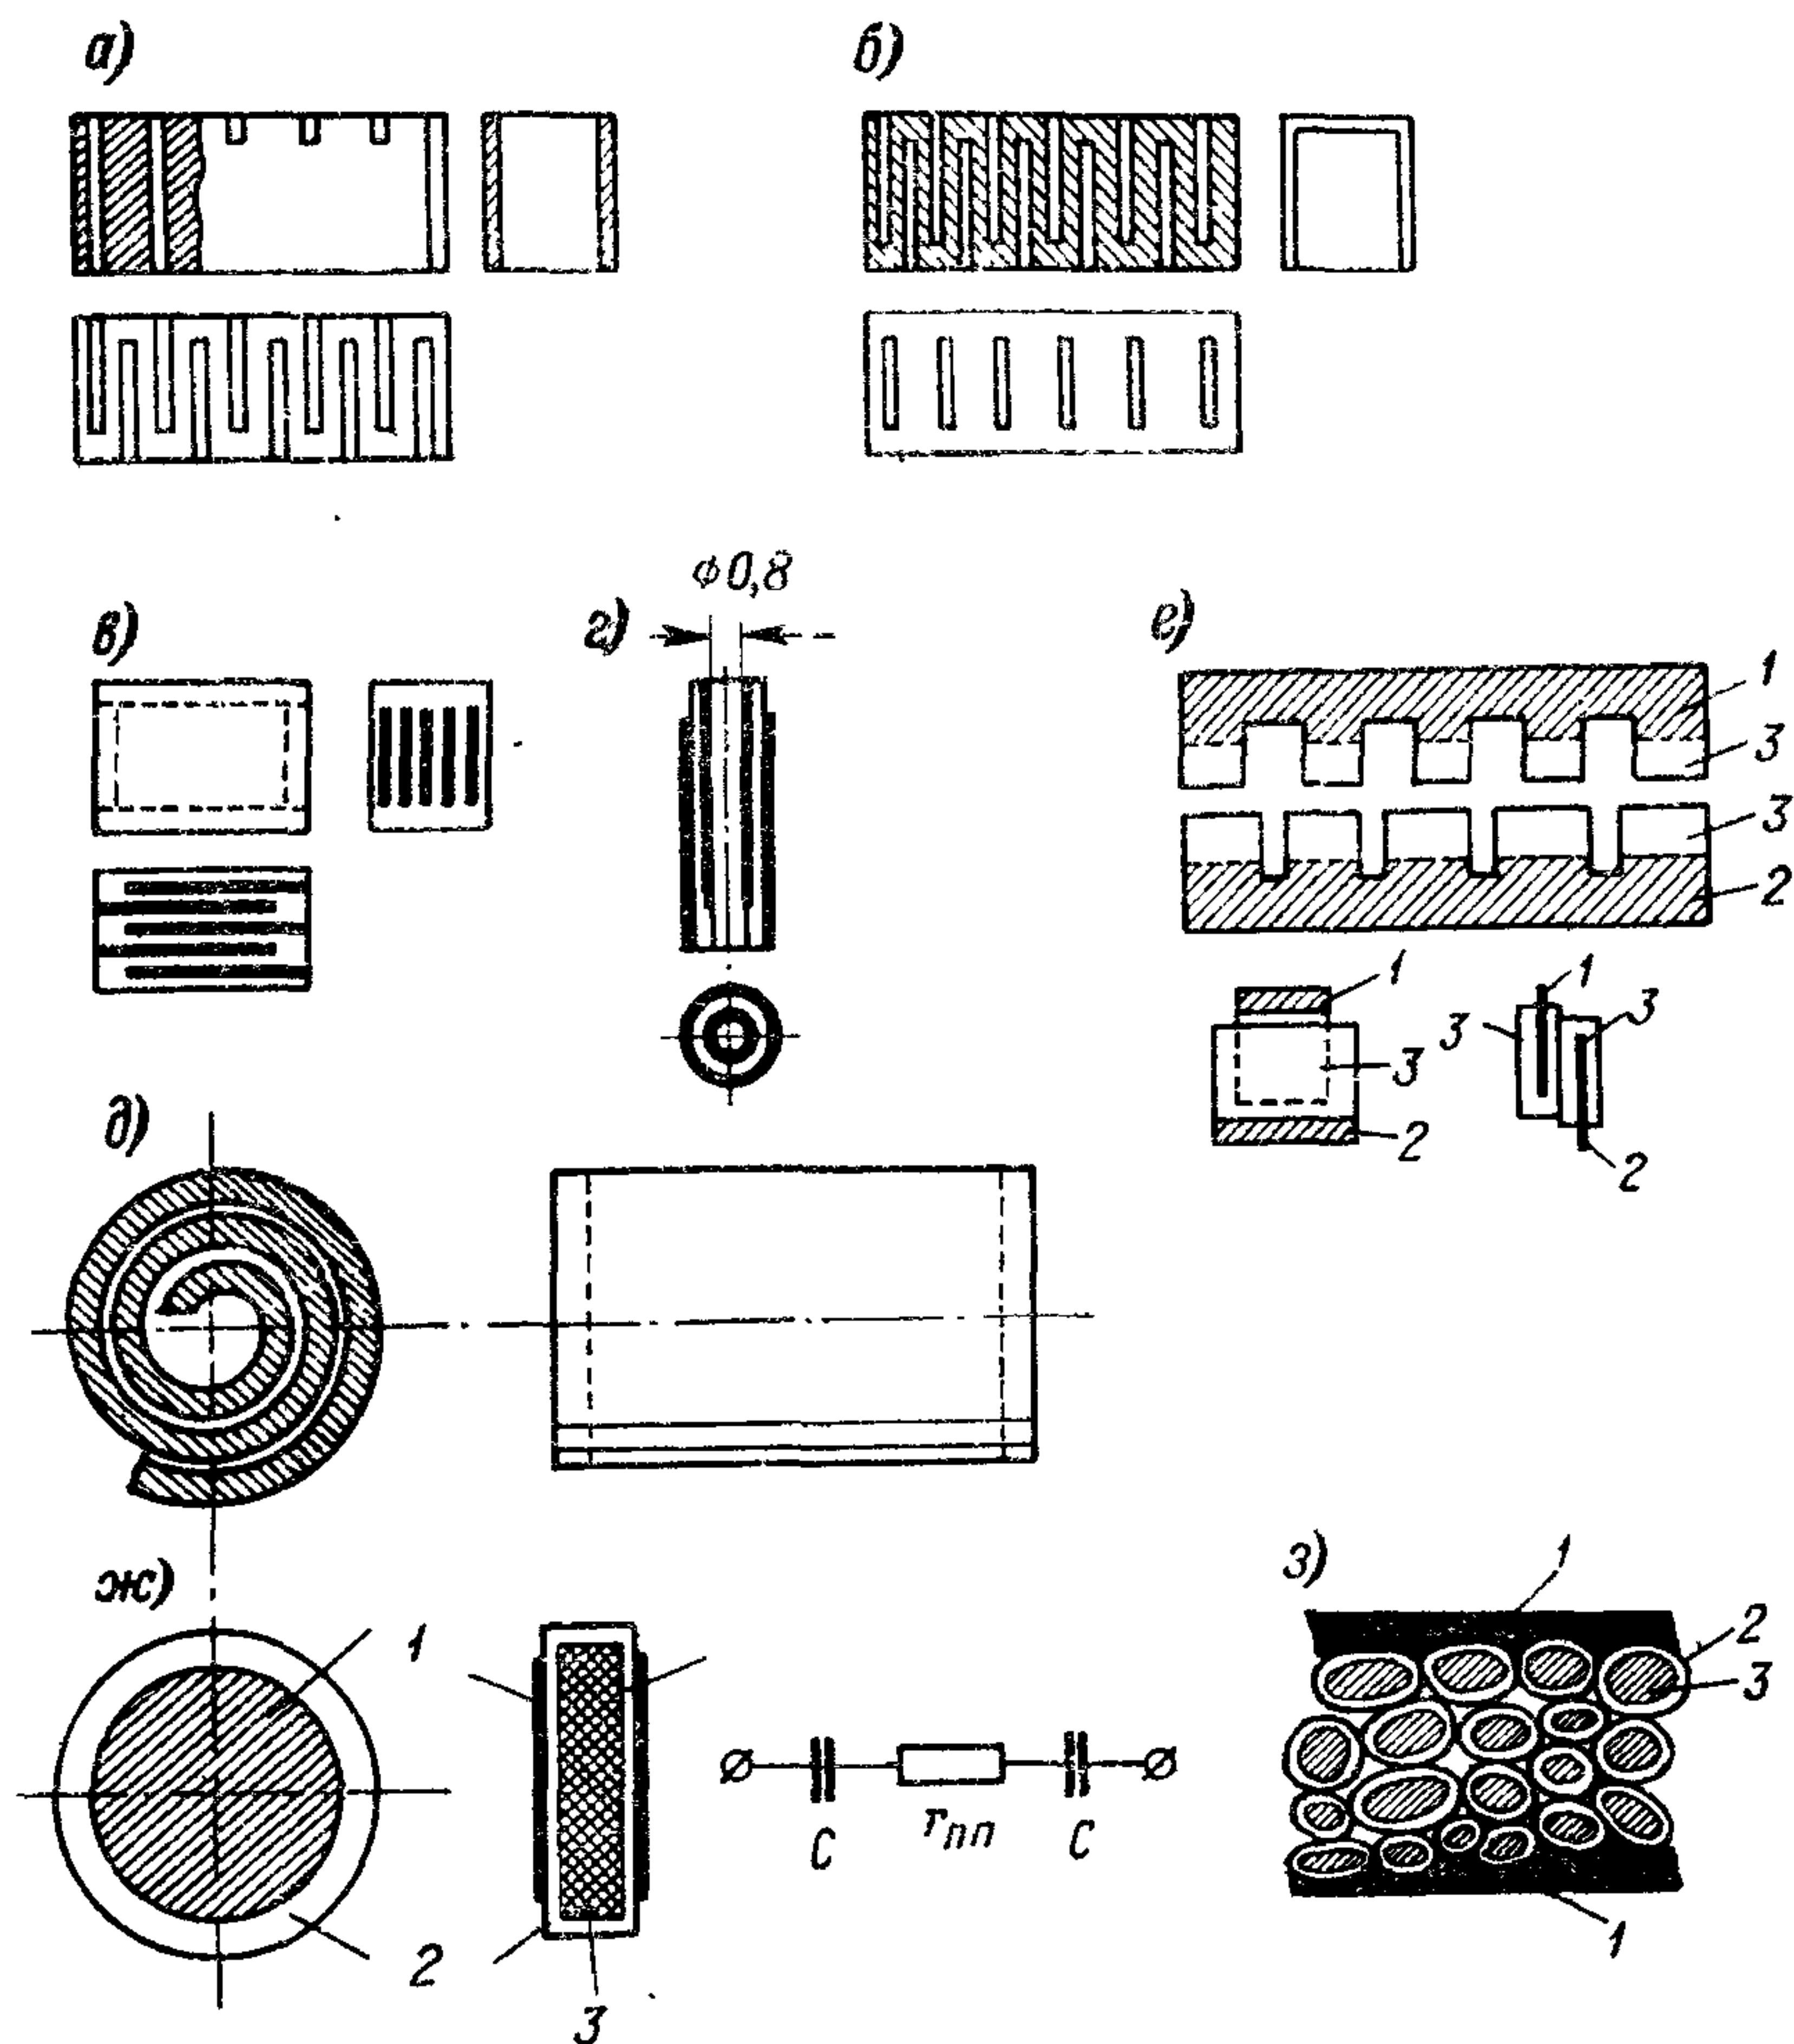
Схемы конструкций конденсаторов с увеличенной удельной емкостью: а — секционный со сквозными прорезями; б — секционный с глухими прорезями; в — монолитный; г — церафил; д — церол; е — фольговокерамический (1 — фольга с узкими зубцами; 2 — фольга с широкими зубцами; 3 — слой шликера на фольге); ж — с барьерным слоем; з — с пограничным слоем.
